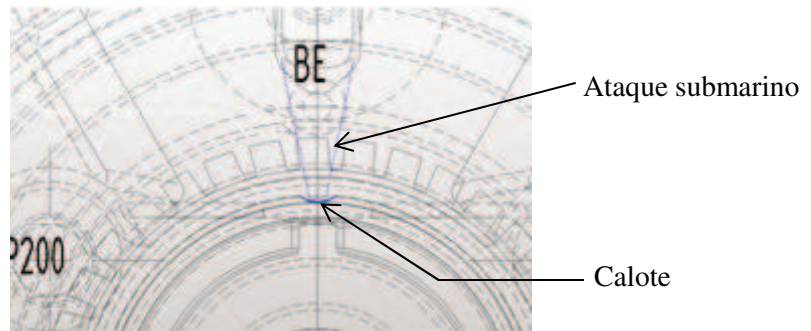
Pormenor da calote em planta (retirado do 2D).
